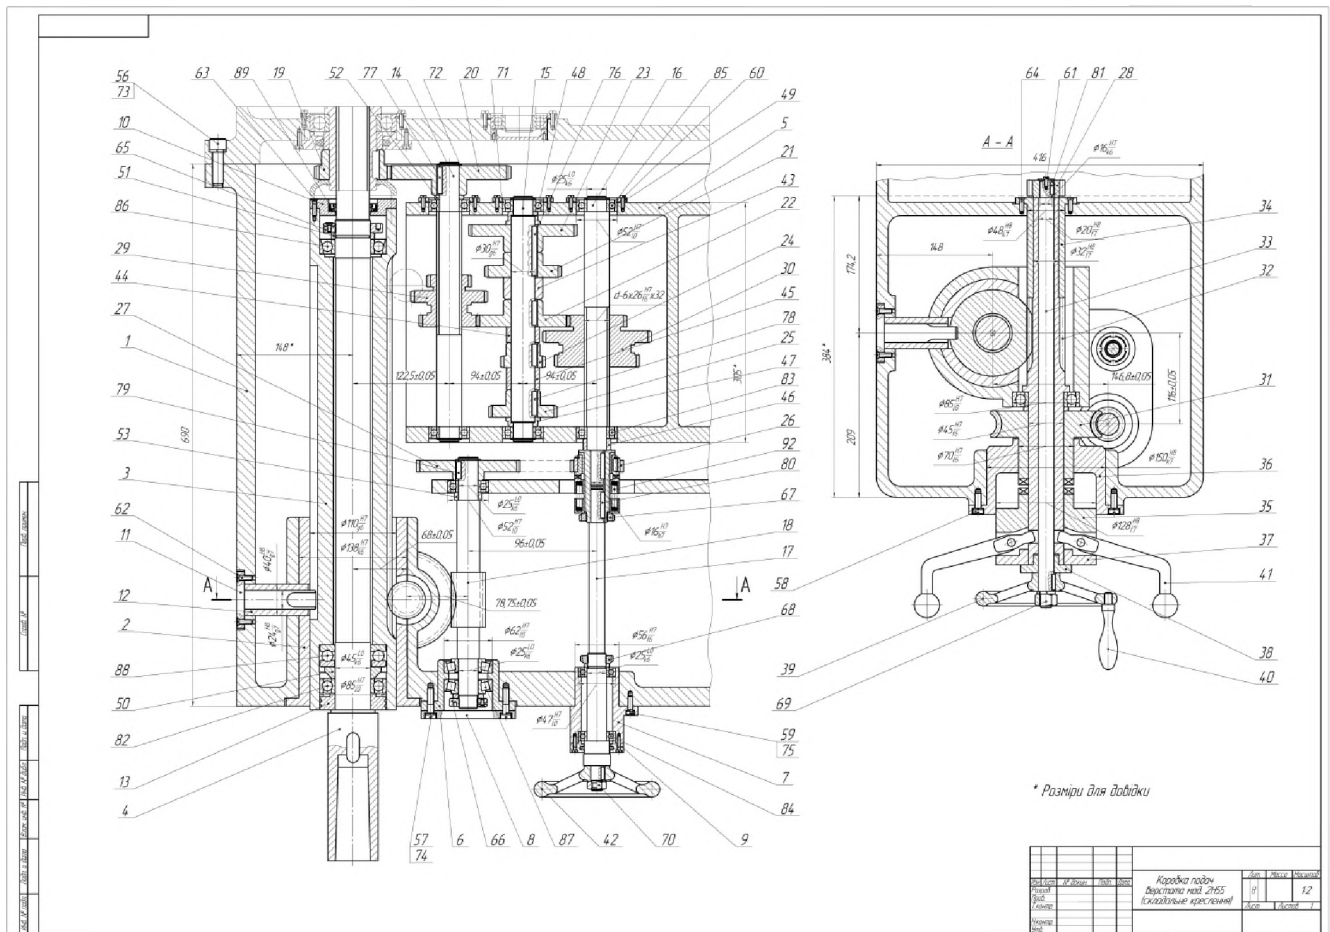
Креслення коробки подач верстата мод. 2Н55
